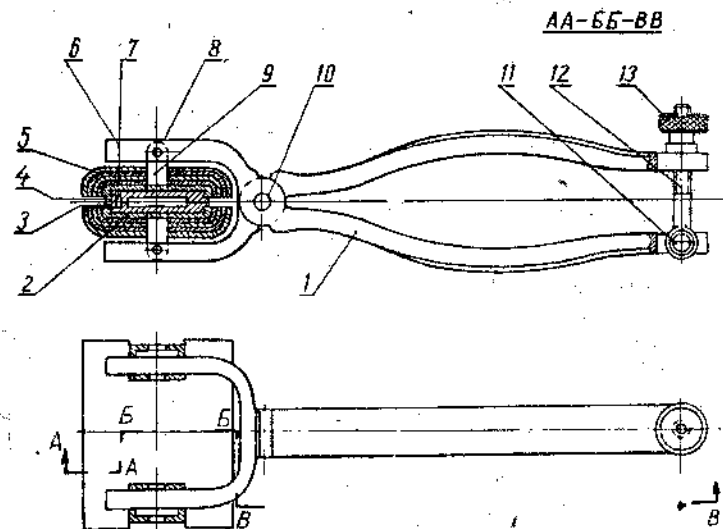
Приспособление для контактной сварки деталей из фторопласта:
